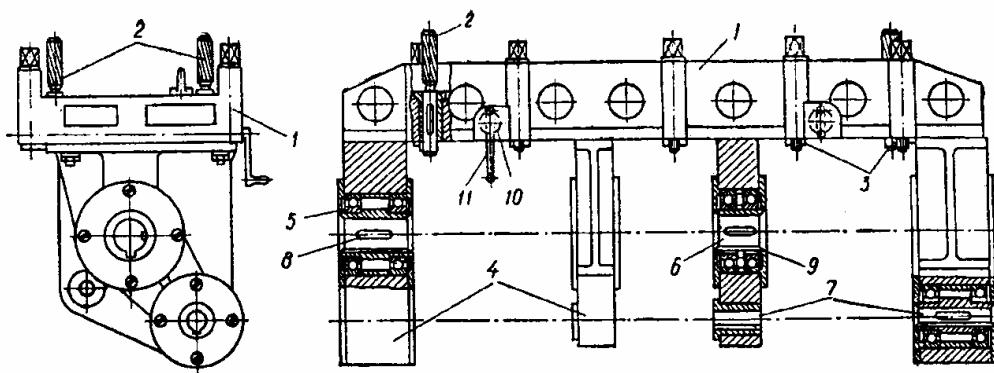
Пристрій (кондуктор) для розточування гнізд корінних підшипників блока циліндрів: 1 – корпус; 2 – установочні штифти; 3 – пластини; 4 – опорні кронштейни; 5 і 7 – підшипники; 6 – напрямні втулки; 8 – шпонки; 9 – пази; 10 – ексцентрики; 11 – рукоятка
